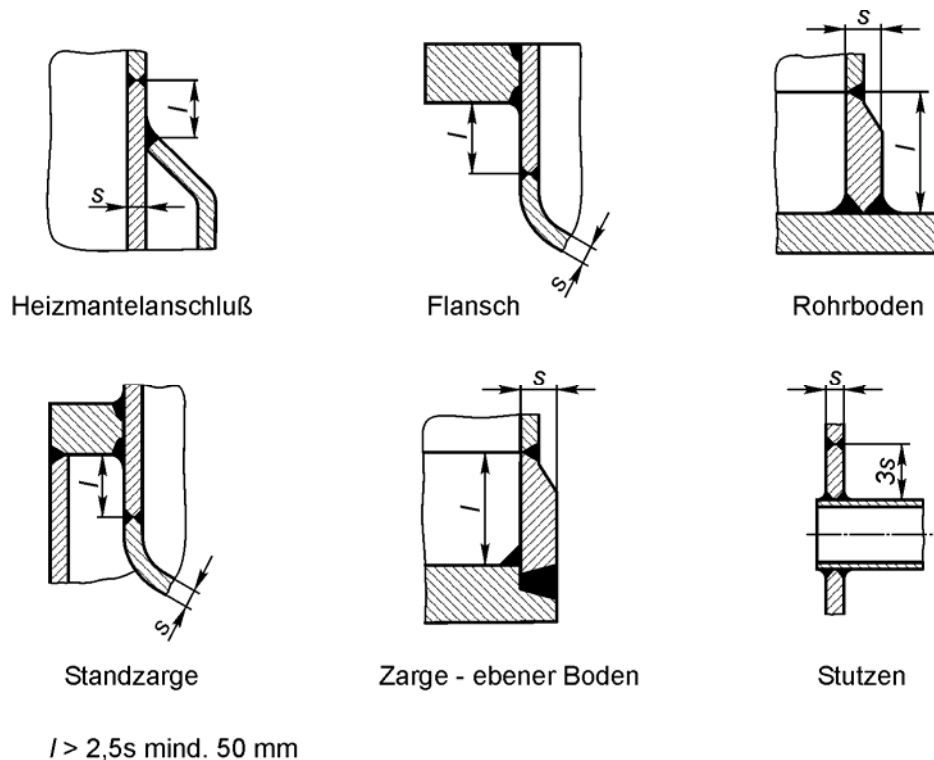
Mindestabstände für Schweißverbindungen
